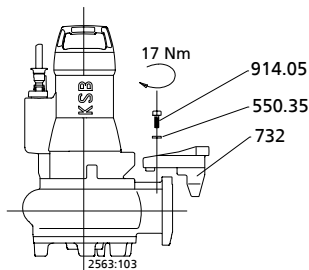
Установка крепления при тросовых направляющих, 1 направляющей штанге и хомуте.
